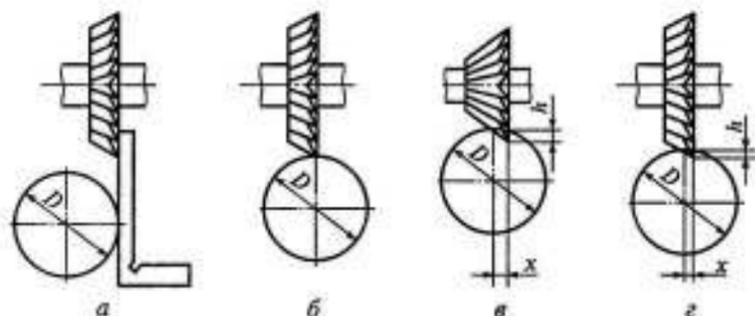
Схема установок фрез при фрезеровании канавок режущих инструментов:
